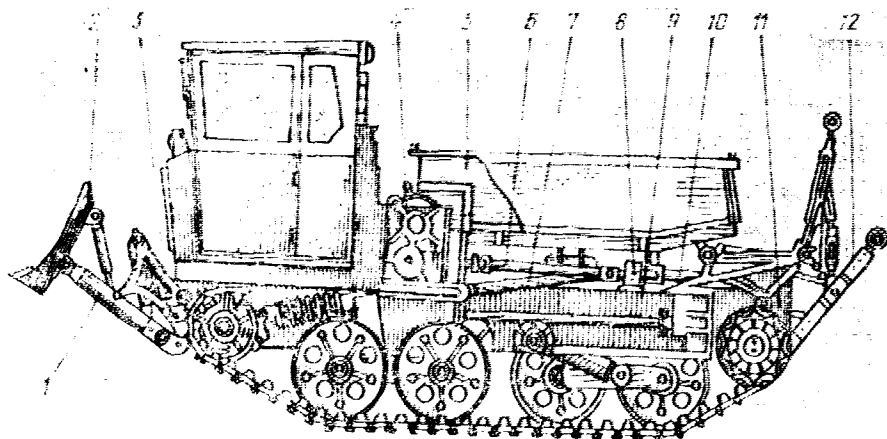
Трактор лесохозяйственный ЛХТ-55: 1 — передняя навеска; 2 — толкатель; 3 — ВОМ трактора; 4 — лебедка; 5 — платформа; 6, 7, 10 — карданный вал; 8 — редуктор привода лебедки и заднего ВОМ; 12 — механизм задней навески
